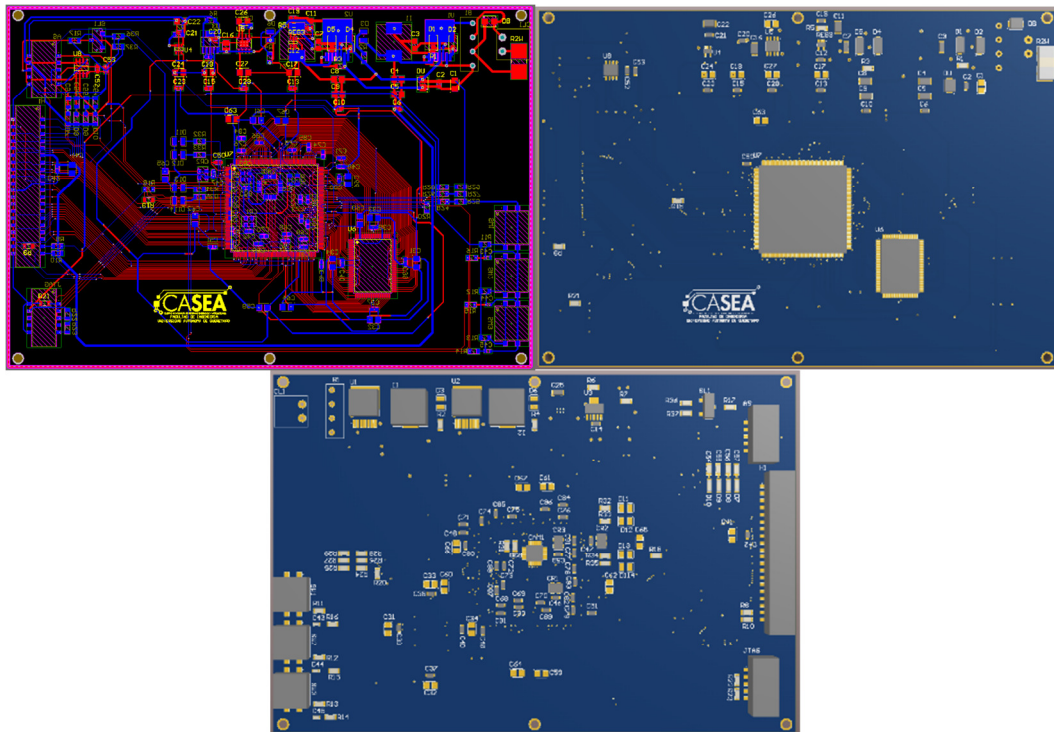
Ruteo del PCB (Arriba izquierda), vista 3D de la cara superior (Arriba derecha) y vista 3D de la cara inferior (Abajo).
